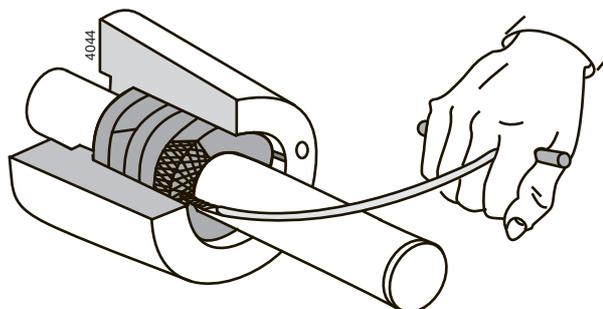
Извлечение уплотнительных колец из корпуса сальника.
